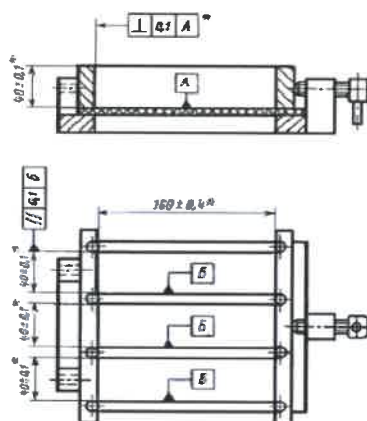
Чертеж формы с допусками и посадками
